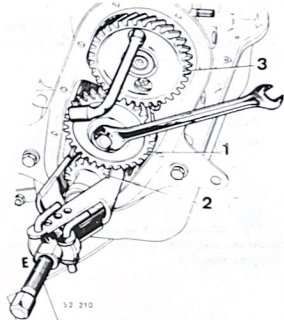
Conjunto de engranes de la distribución en el motor tipo 801.
